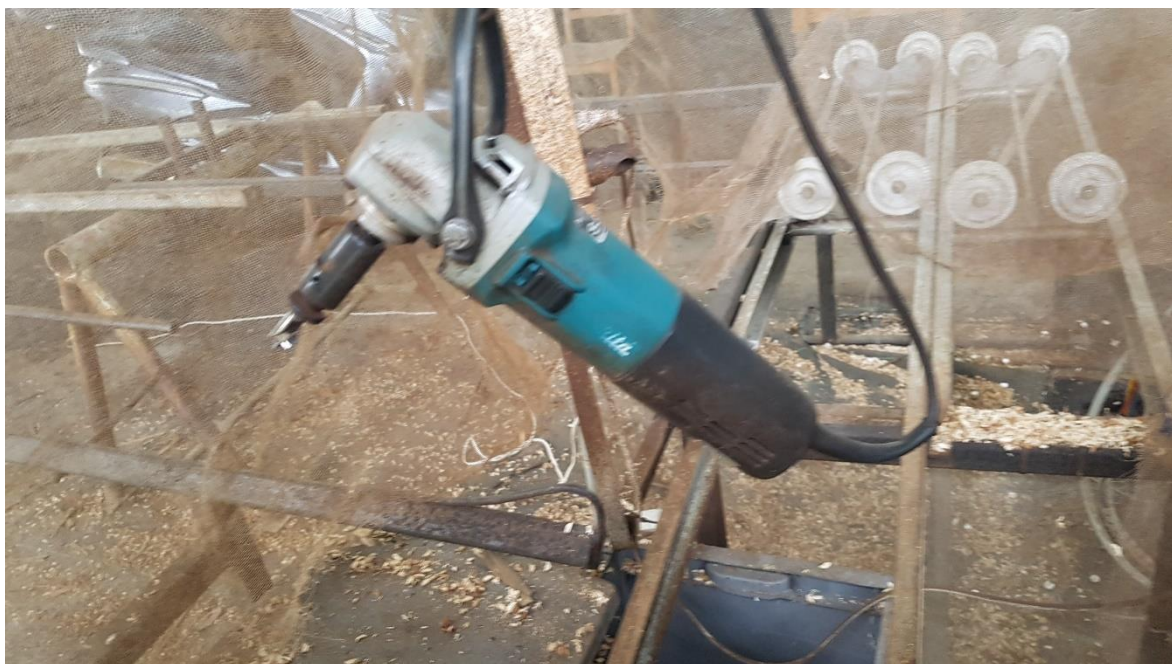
Zona de produção (posto da furação) – Vista de pormenor
